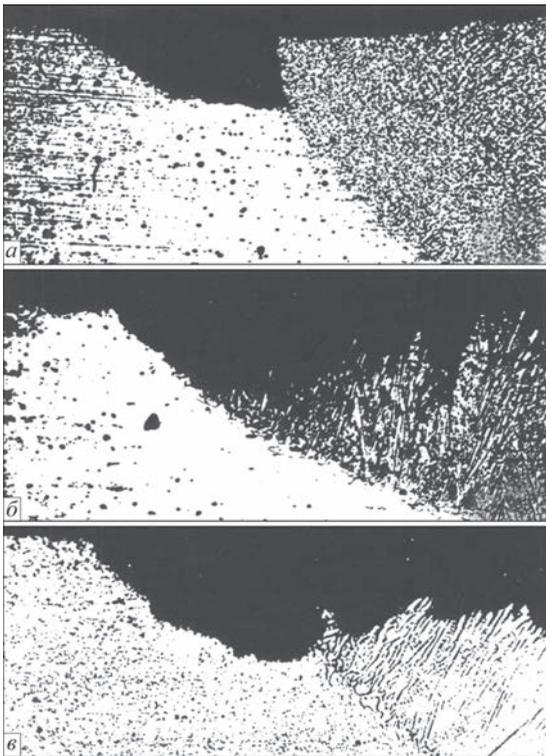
Ножевая коррозия сварных соединений в производстве нитрофоски: *a* — сварное соединение стали 10Х17Н-13М3Т (электроды ЭА-400/(10у): $\times 100$; *b* — сварное соединение сплава 06ХН28МДТ (электроды ХЛ-1): $\times 200$; *v* — сварное соединение стали 03Х21Н21М4ГБ (электроды 03Л-17У): $\times 100$
